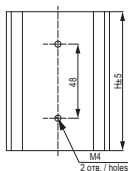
Габаритные и установочные размеры радиатора / Figure 12 - Overall and mounting dimensions of the heat sink /
